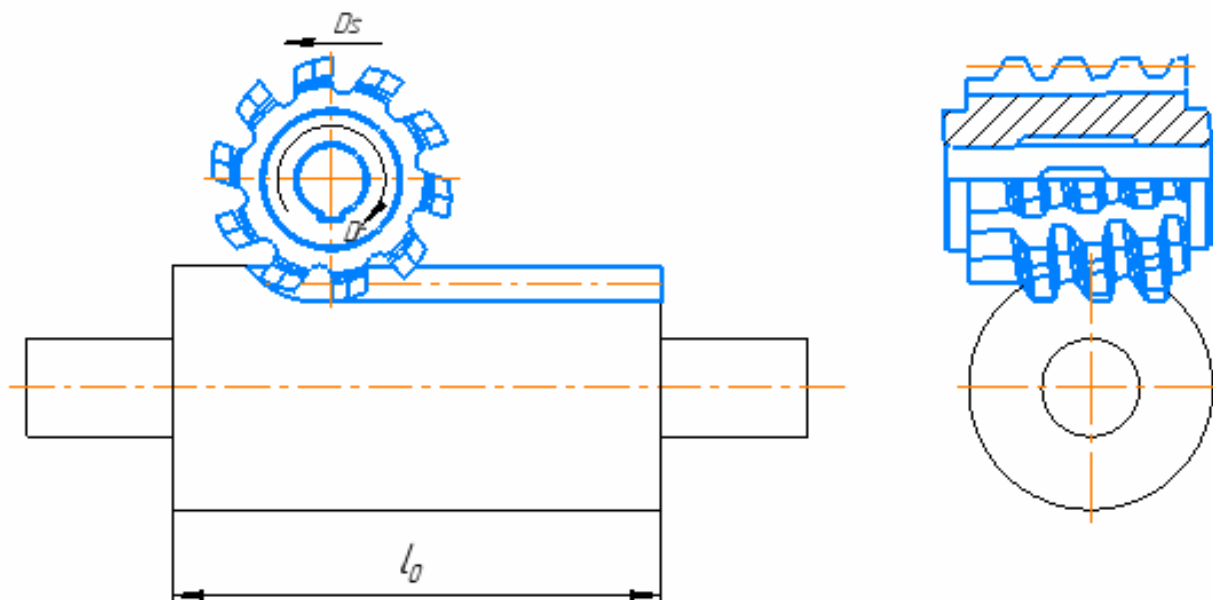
Схема фрезерования шлицевого вала червячно-шлицевой фрезой
